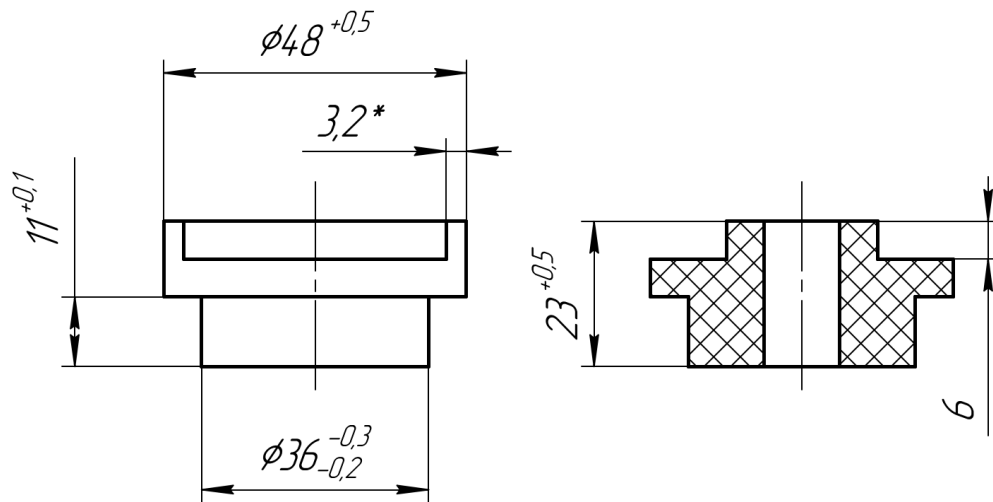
Робоче креслення розробленої ексцентрикової деталі
